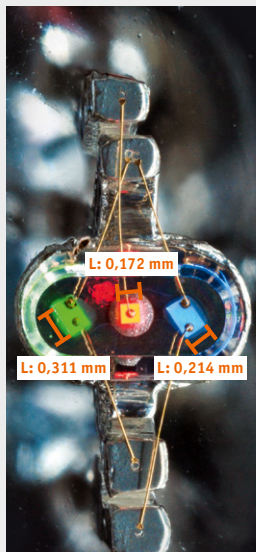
Die LEDs sind nur wenige Zehntelmillimeter groß.
